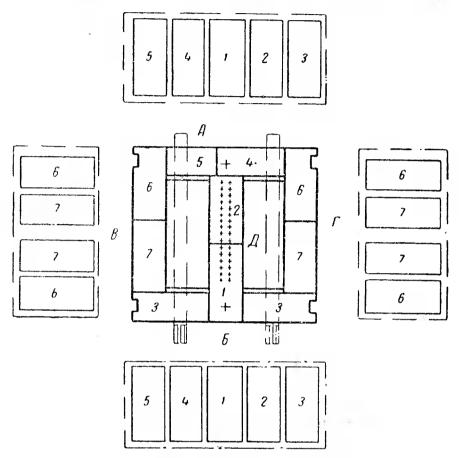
Расстановка рабочих и раскладка пластин во время сборки мощных магнитопроводов.
